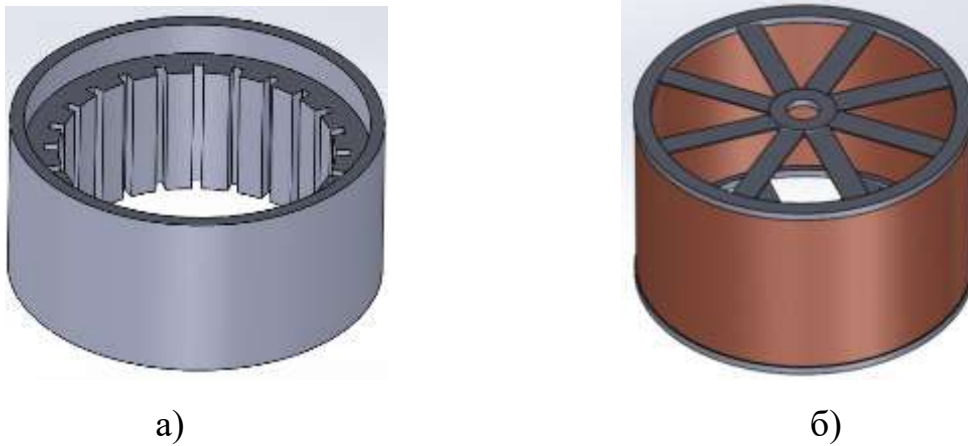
Вид деталей диференціалу, створених в програмі Solid Works: а – статора основного електродвигуна з корпусом, б – сателіт (проміжний ротор) з вентилятором.
